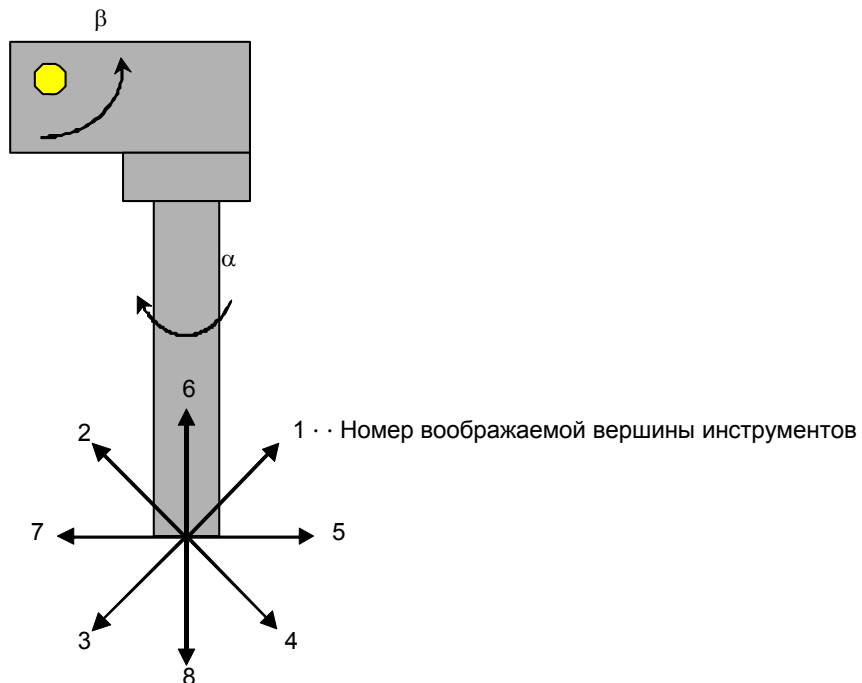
(e) Связь между номером воображаемой вершины инструмента и направлением
